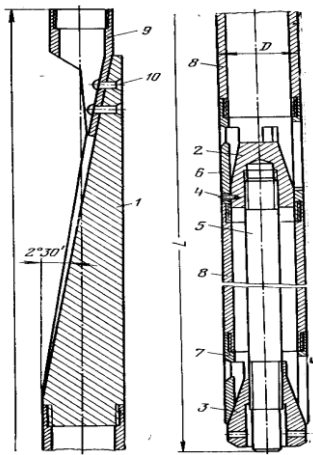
Стационарный клин КОС: 1 – клин; 2,3 – распорные конусы; 4 – срезная шпилька; 5 – шток; 6,7 – распорные патрубки; 8 – соединительные патрубки; 9 – установочная труба; 10 – заклёпки.
